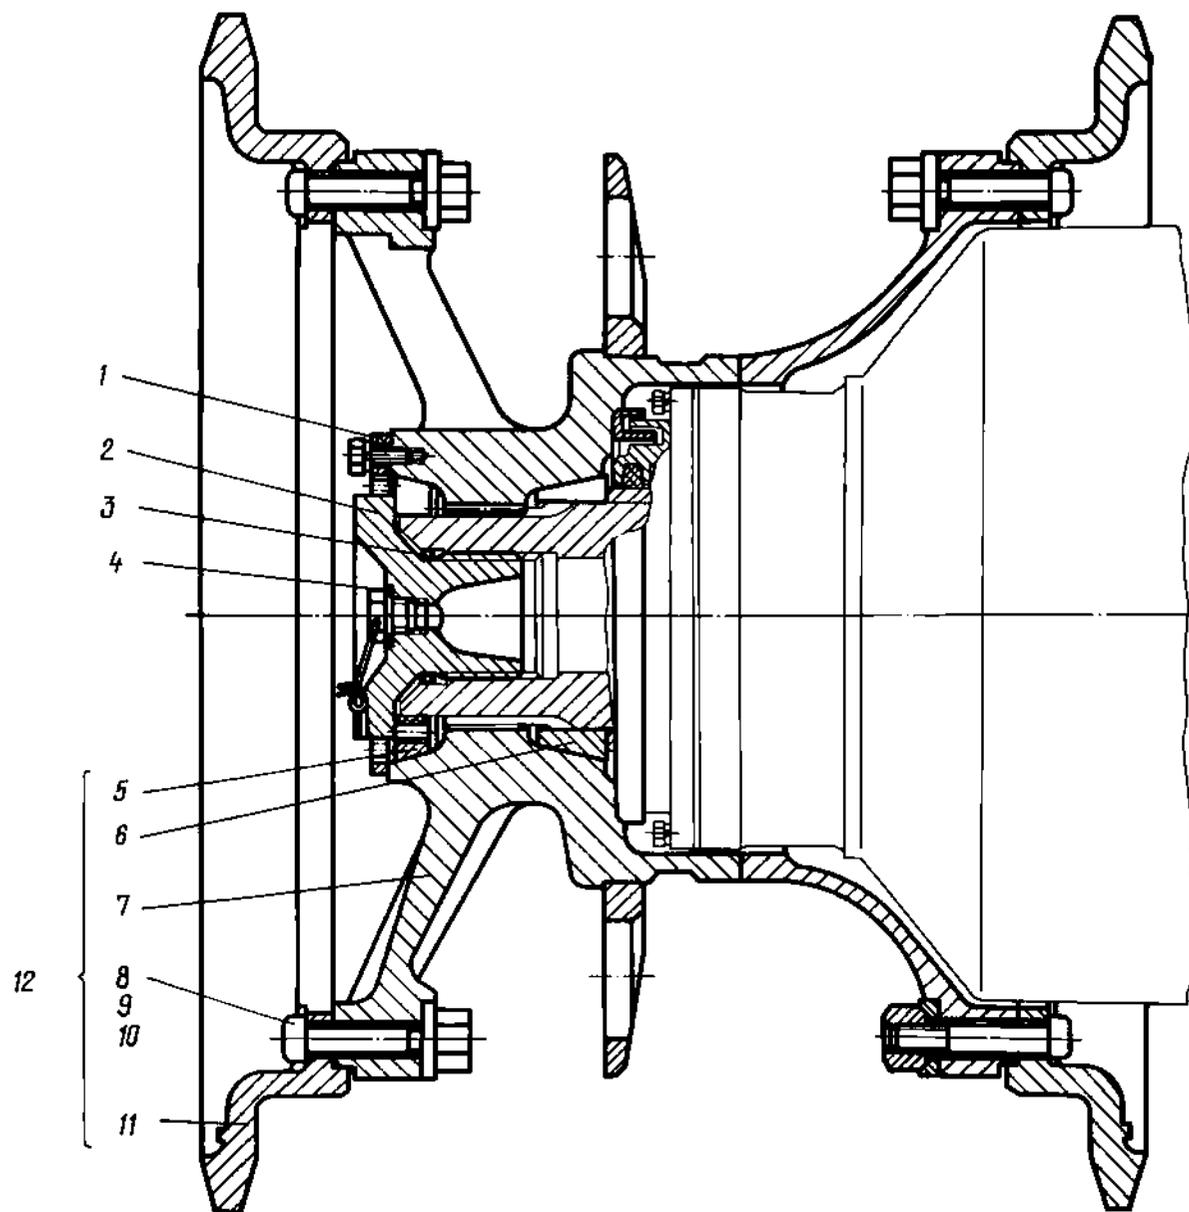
МОНТАЖ КОЛЕСА ВЕДУЩЕГО 172.54с6
